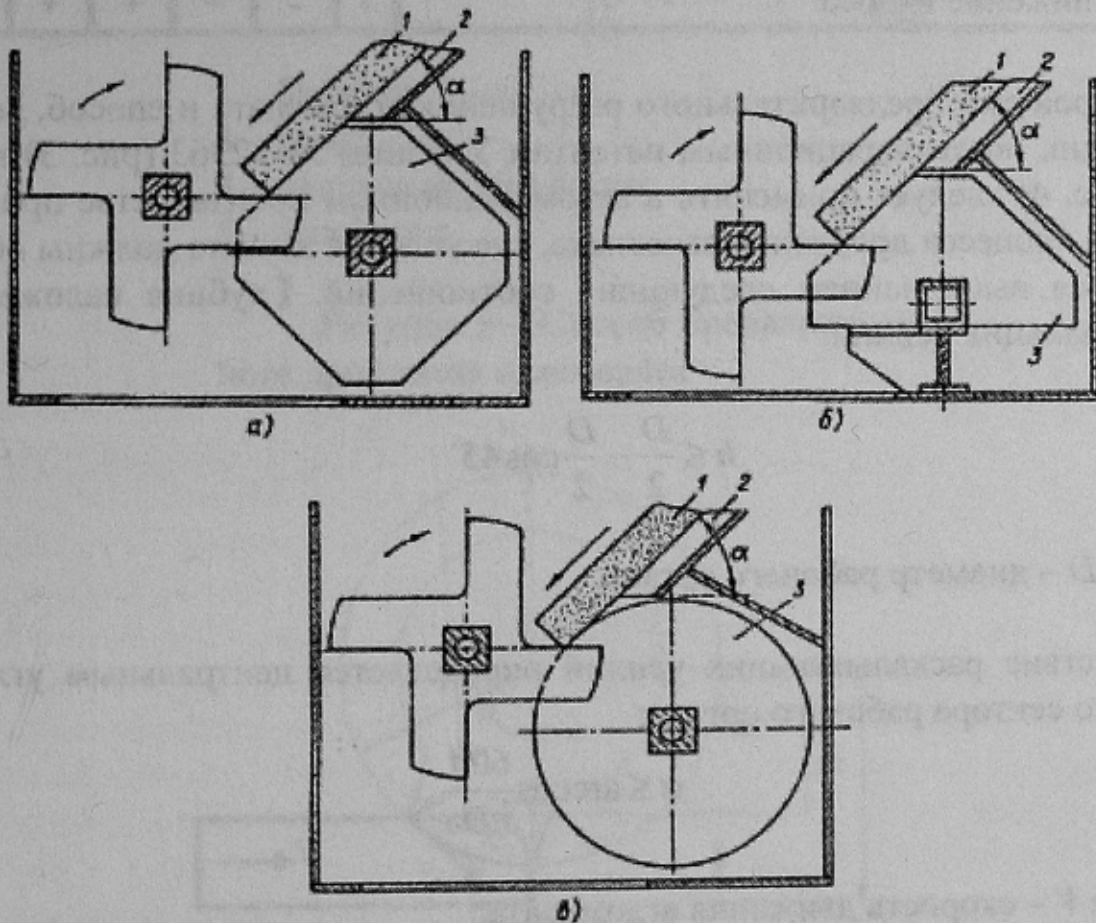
Конструктивные схемы одновалковой зубчатой дробилки с консольно расположенными колосниками: а) одновалковая дробилка с четырехпозиционными колосниками; б) одновалковая дробилка с круглыми колосниками; в) одновалковая дробилка с двухпозиционными колосниками; 1 – агломерат; 2 – наклонная направляющая; 3 – колосники.
